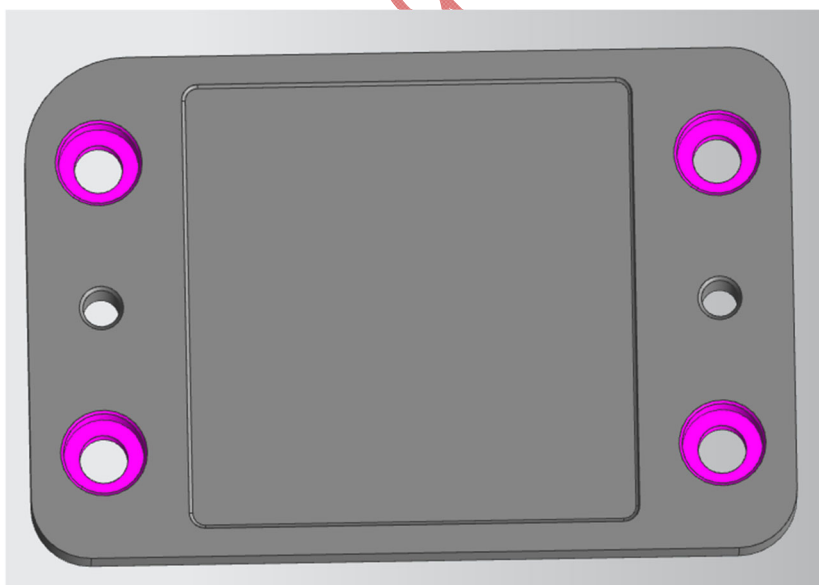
3D-Zeichnung eines Prototyp-Werkzeugeinsatzes
